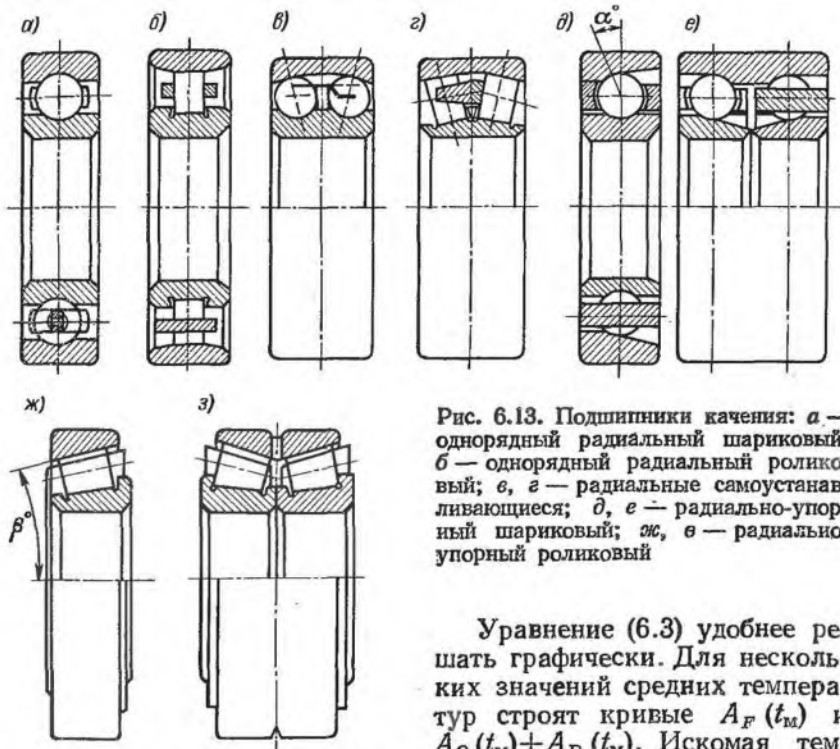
Подшипники качения: а — однорядный радиальный шариковый; б — однорядный радиальный роликовый; в, г — радиальные самоустанавливающиеся; д, е — радиально-упорный шариковый; ж, з — радиально-упорный роликовый
